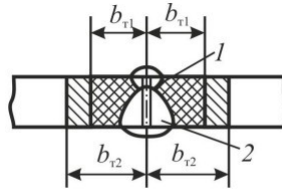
Типова схема багаторохідного шва, де проходи мають різну қп.
